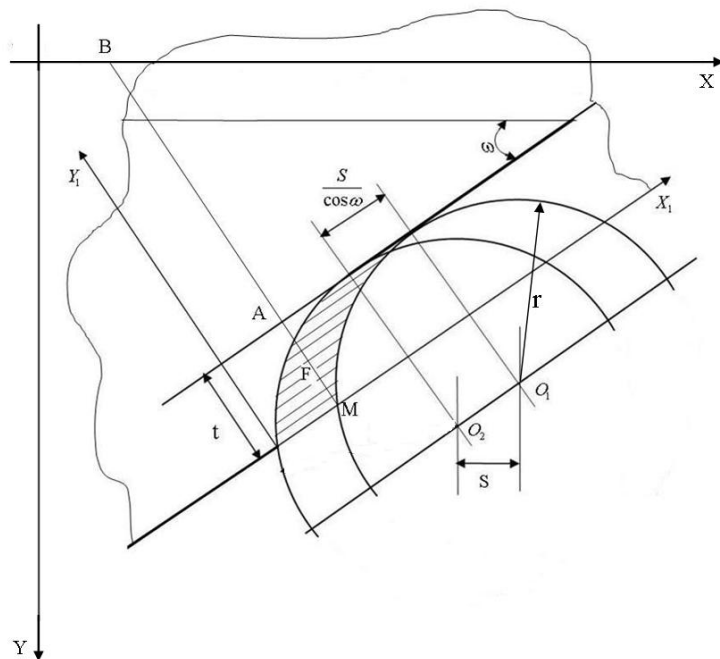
Схема снятия припуска резцом с круглой режущей пластиной на конической части заготовки при выходе резца из впадины обрабатываемого профиля
